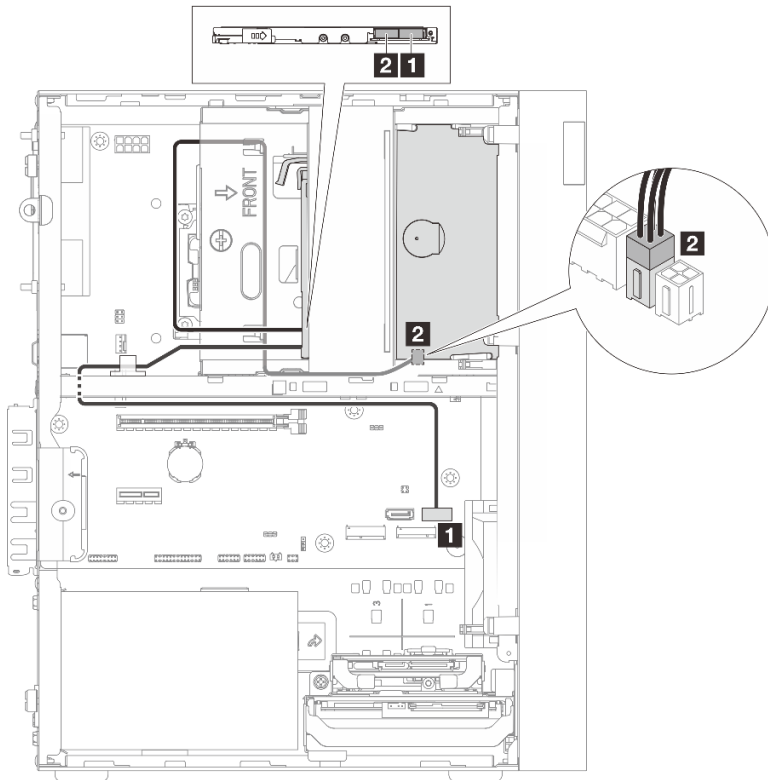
Kabelführung für optisches Plattenlaufwerk
